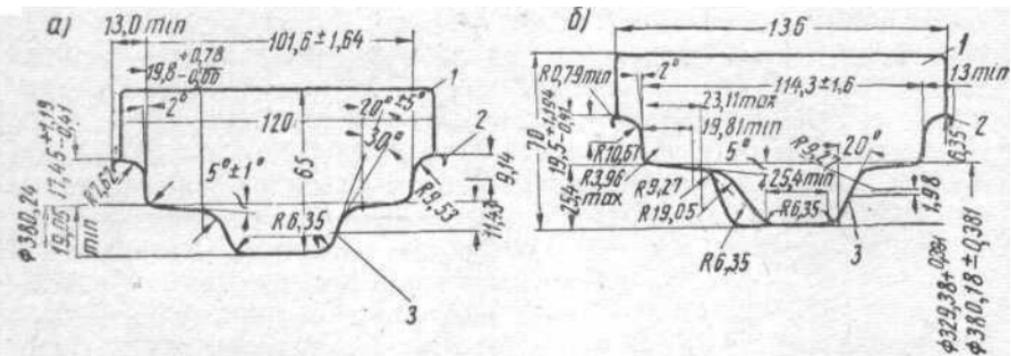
Шаблоны для проверки профиля обода колеса:
